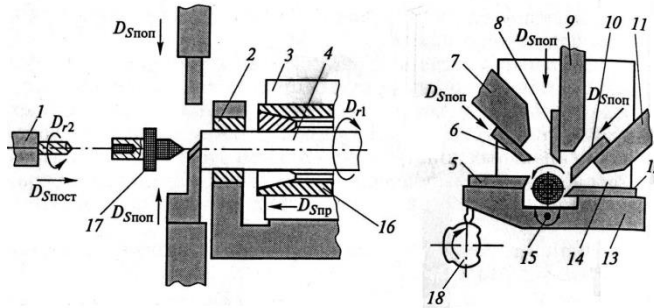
Схема обробки заготовки на автоматі поздовжнього точіння:
